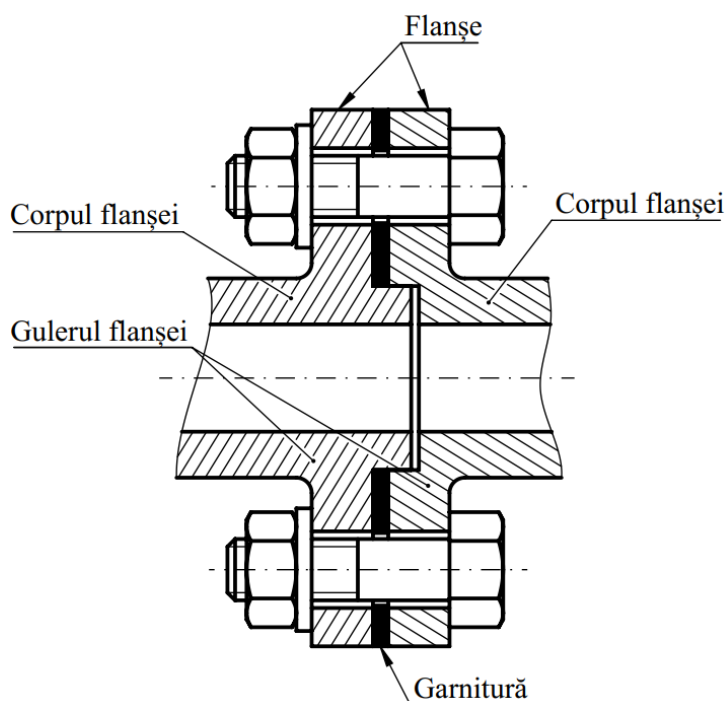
Reprezentarea asamblării cu flanșe prin intermediul șuruburilor și a piulițelor
